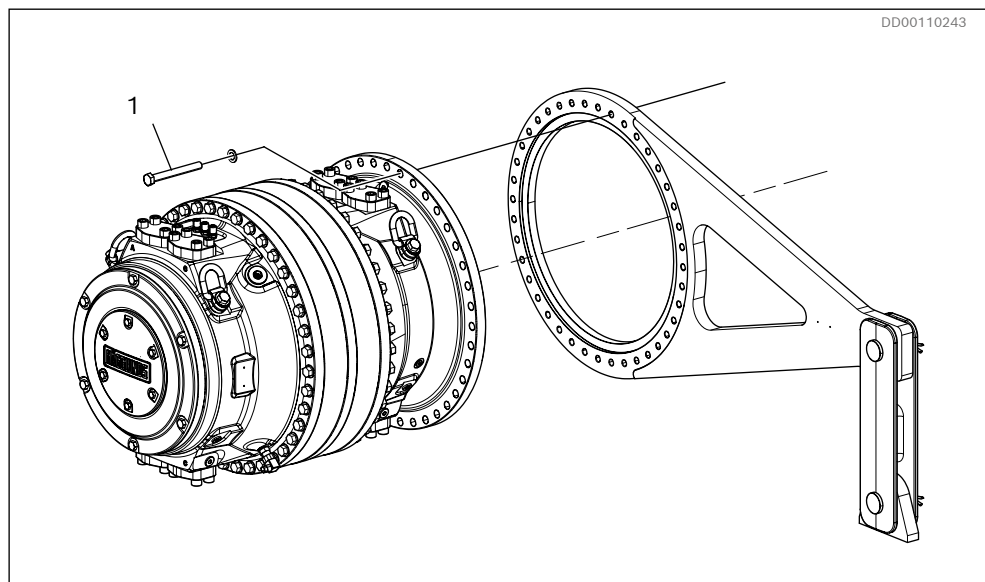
Exemplo, montagem do braço de torque de uma terminação TC A 0400 para CBp 400 F
